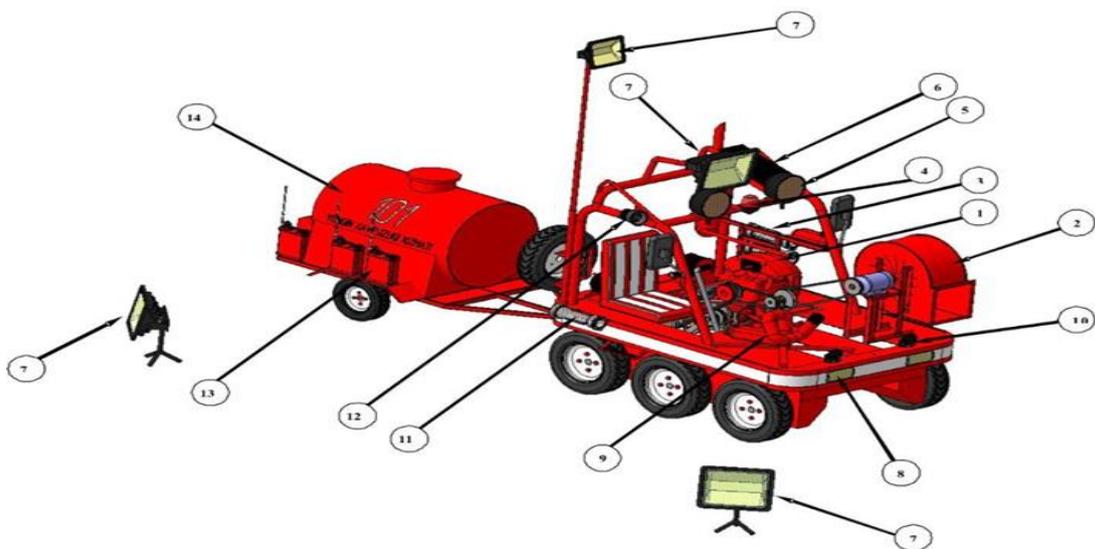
Аксонометрическая схема пожарной техника в предлагаемом образце с разбивкой на детали: 1-двигатель. 2-дымосос. 3-устройство для смешивания пены. 4-оборудования для освещения. 5-прожектор (осветительное устройство) 6-усилитель 12 Вт до 220 Вт, 7-мобильный прожектор. 8-осветительная лампа. 9-лафетный ствол.10-ороситель. 11-соединитель 66 мм. 12-оборудование для усиления звука. 13-разбрызгиватель воды. 14-емкость для воды.
